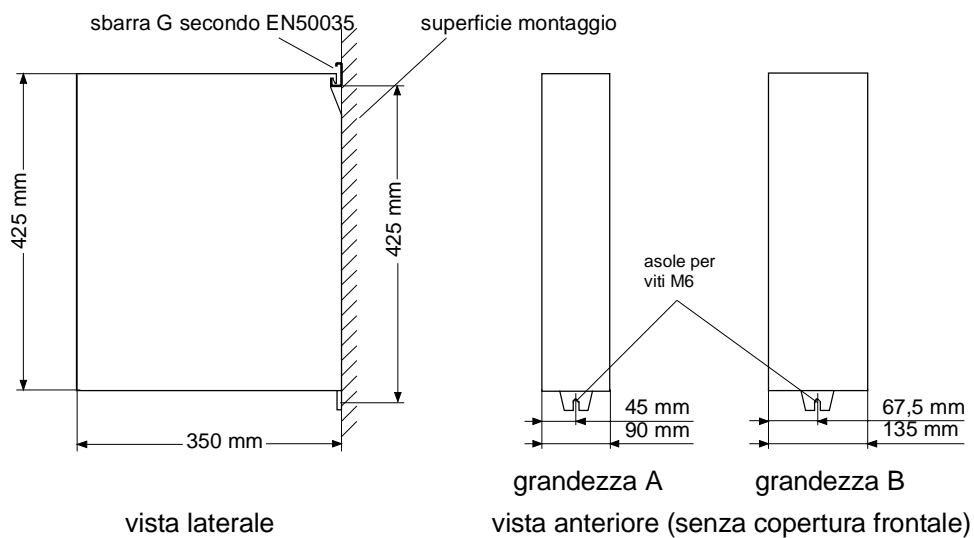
Disegni d'ingombro per montaggio grandezze A, B
